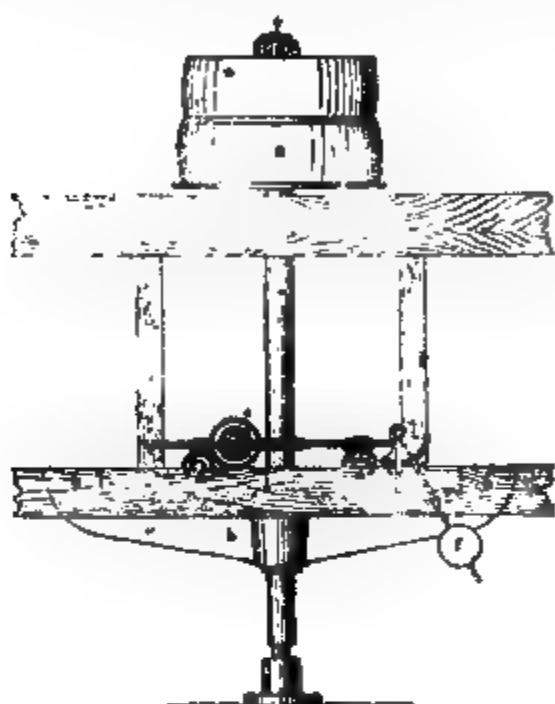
49 Waffer's Holzwool-Hobelmaschine.
